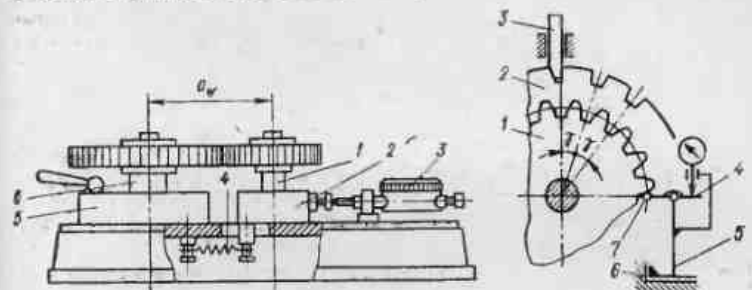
Прибор МЦМ-400Б для комплексной проверки цилиндрических зубчатых колес
